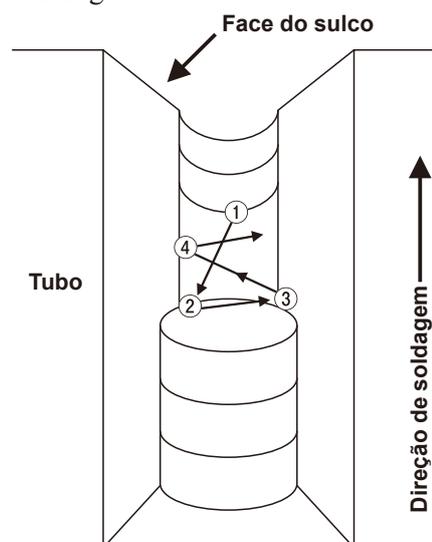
A Técnica de retroceda na soldagem de posição vertical-para cima das tubulações
